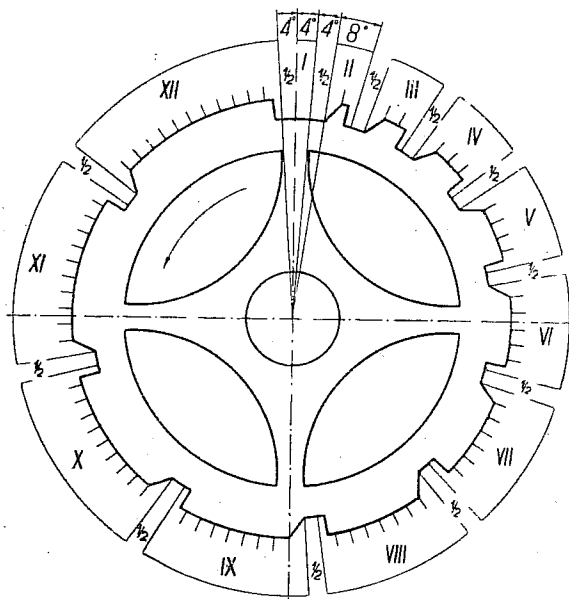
przedstawia podział kołnierza zapadkowego typu pary-
